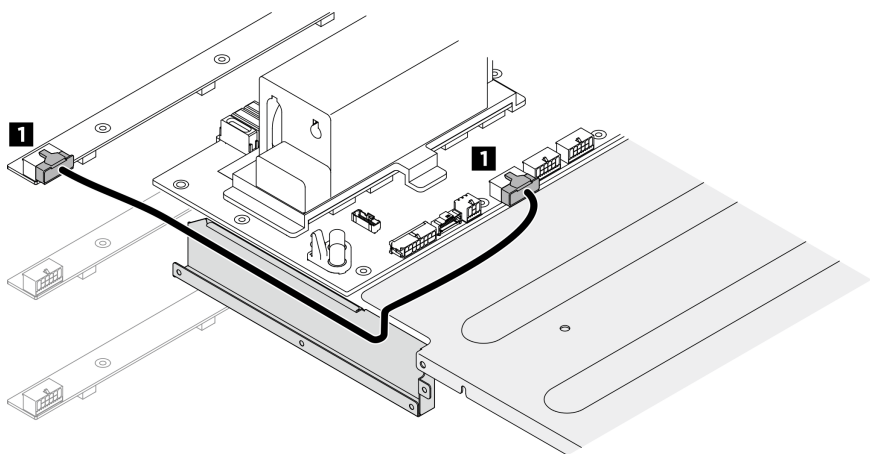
Disposición de los cables de la placa de control del ventilador superior posterior
